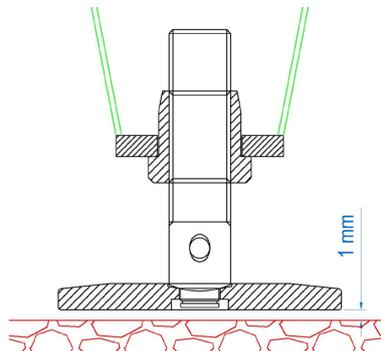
Piedino centrale F in posizione rialzata rispetto al pavimento.
